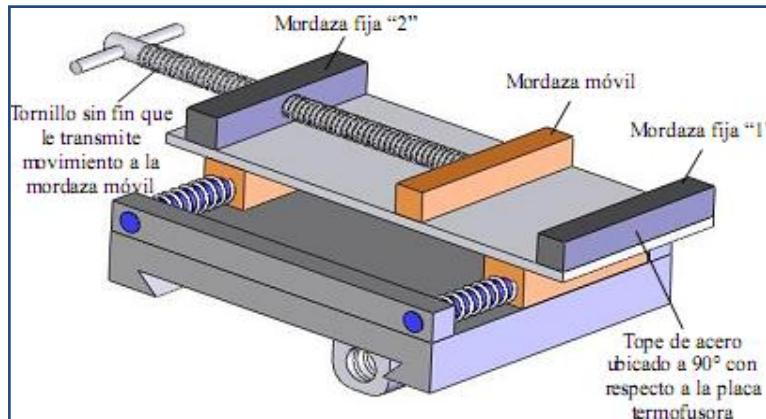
Despiece de máquina soldadora de termoplásticos.
